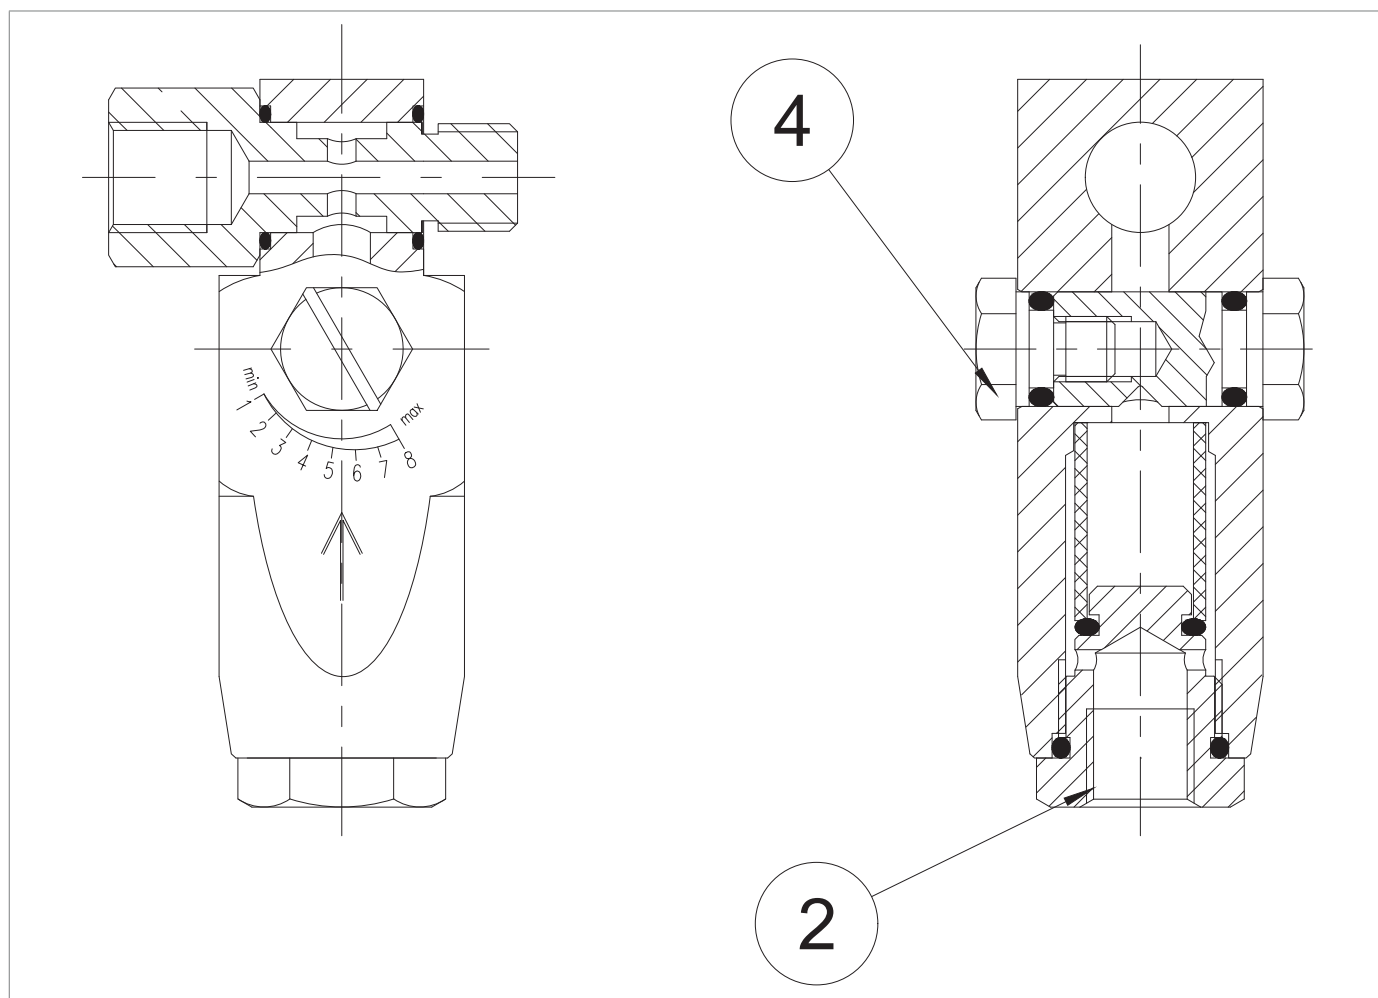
Coppie di serraggio valvola di laminazione AR100
